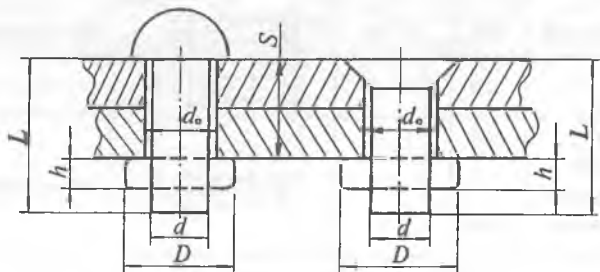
Размеры заклепок и диаметры отверстий под заклепки
